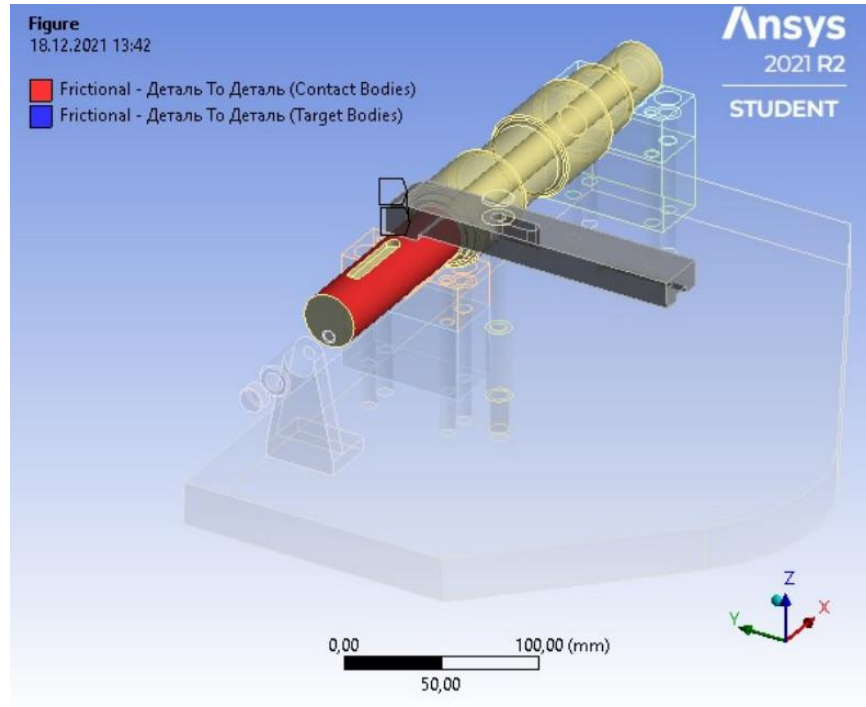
Сполучення між поверхнею заготовки та прихвата
